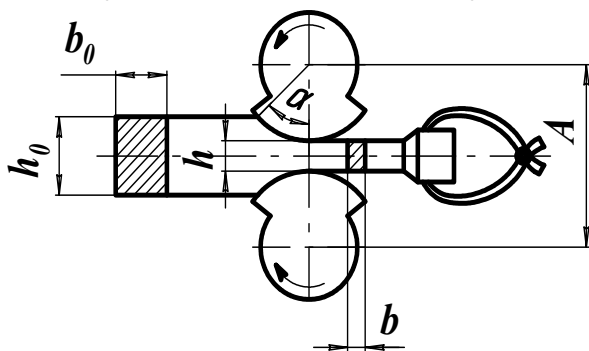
Схема вальцювання: h_0 , b_0 , h , b – висота і ширина заготовки до і після вальцювання
